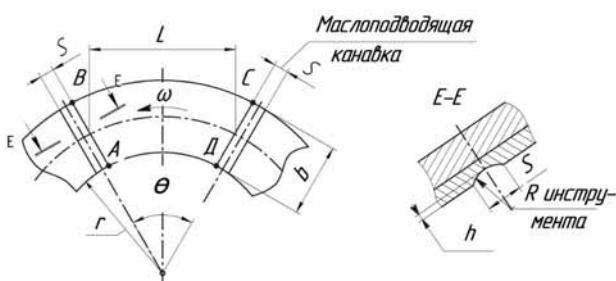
Секторная подушка предлагаемого плоского полукольца осевого подшипника со смазочными канавками
